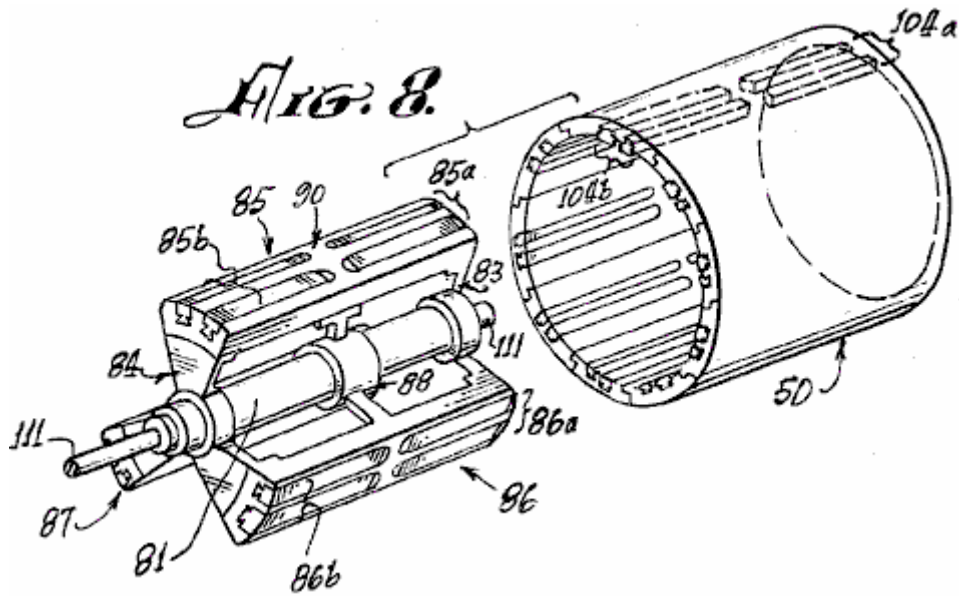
es una vista de perspectiva hecha explotar del rotor y el estator del motor de Fig.3 y Fig.4
